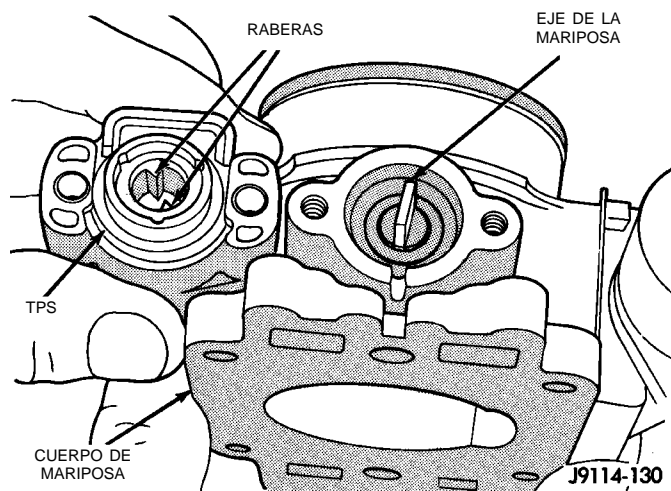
Instalación del sensor de posición de la mariposa del acelerador—Motor de 4.0L
